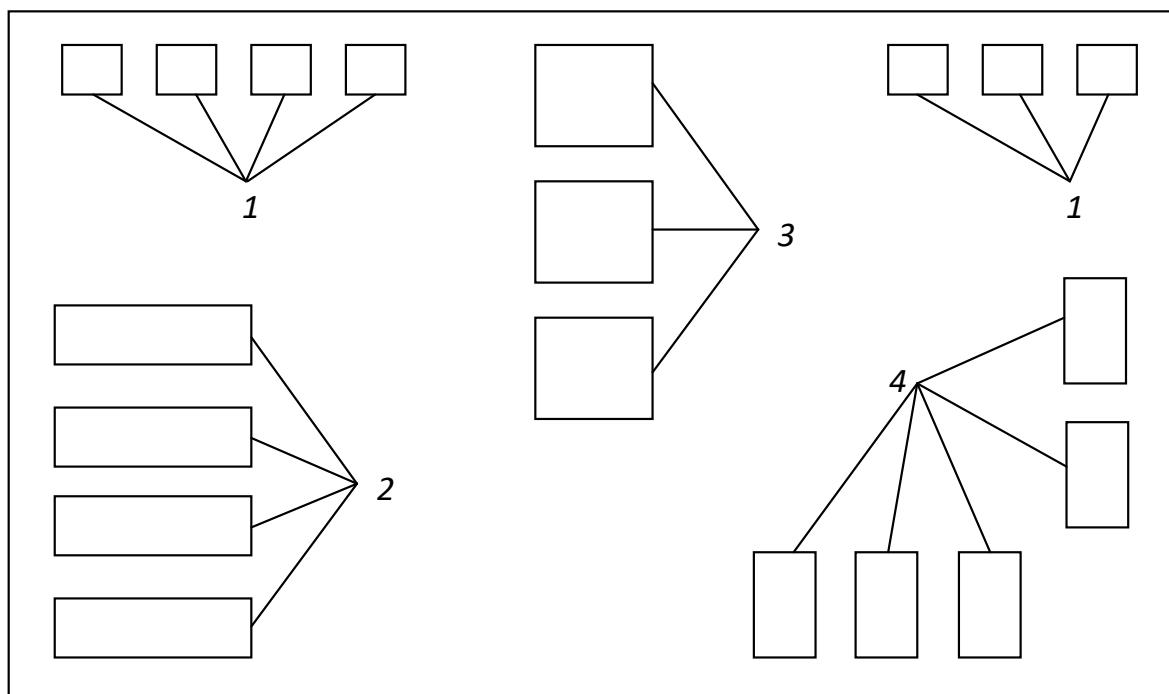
План расстановки оборудования ремонтного цеха: 1 – сверлильный станок; 2 – расточный станок; 3 – сверлильный станок; 4 – токарный станок
